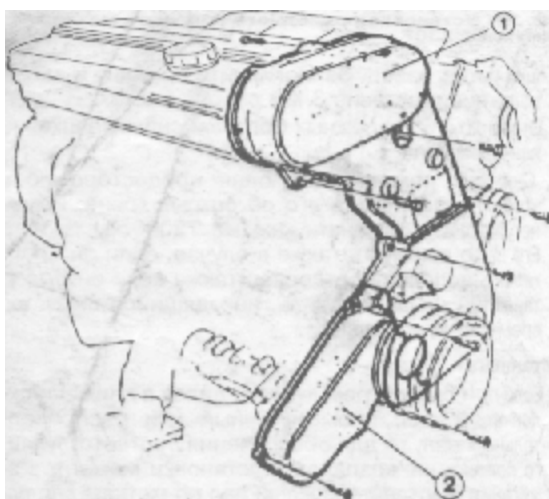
Верхняя (1) и нижняя (2) крышки приводного ремня — Двигатель В234F
